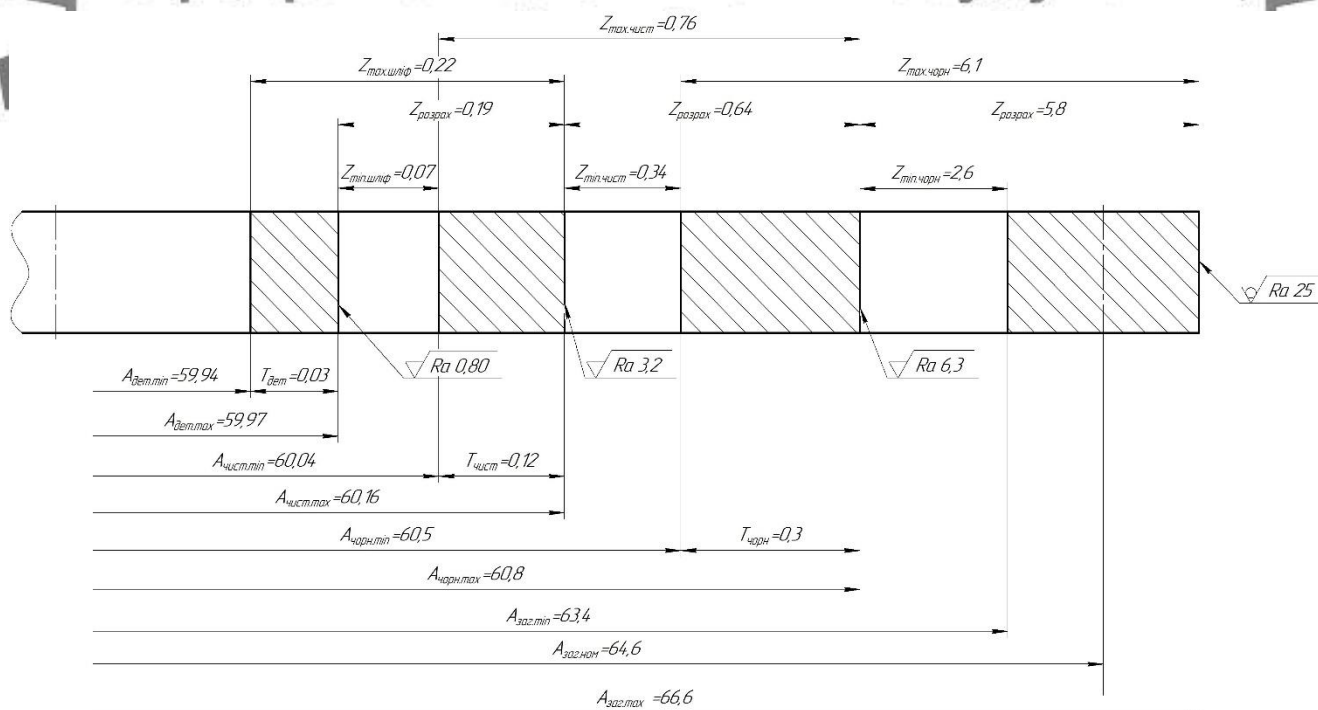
Схема розташування допусків та припусків на розмір $\varnothing 60 f7(-\frac{0,03}{-0,06})$ мм.
